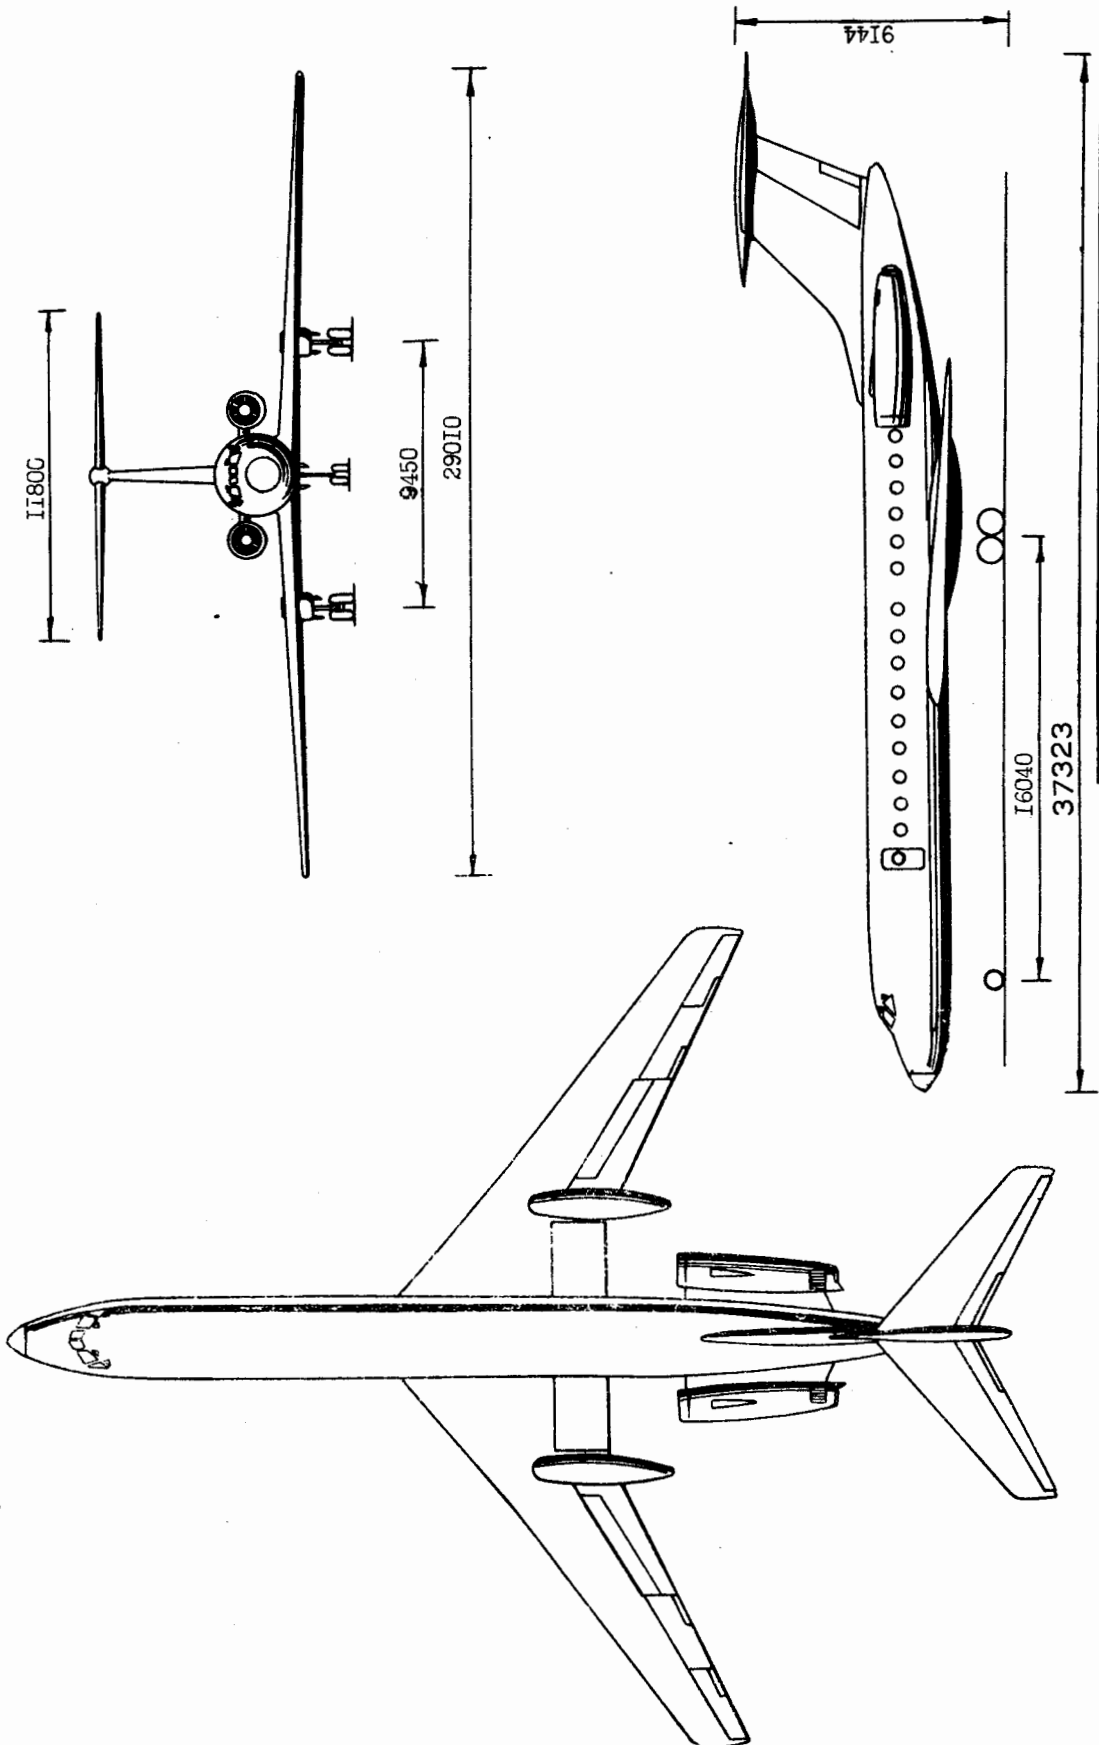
Gesamtansicht des Flugzeuges Tu 134A in drei Ansichten
